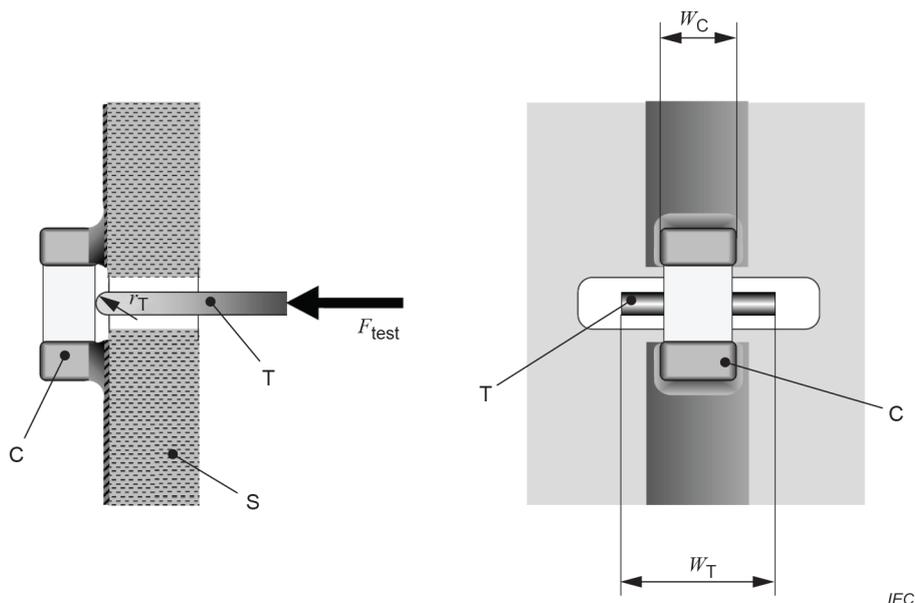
Essai Ue<sub>2</sub>, essai d'arrachement par traction
